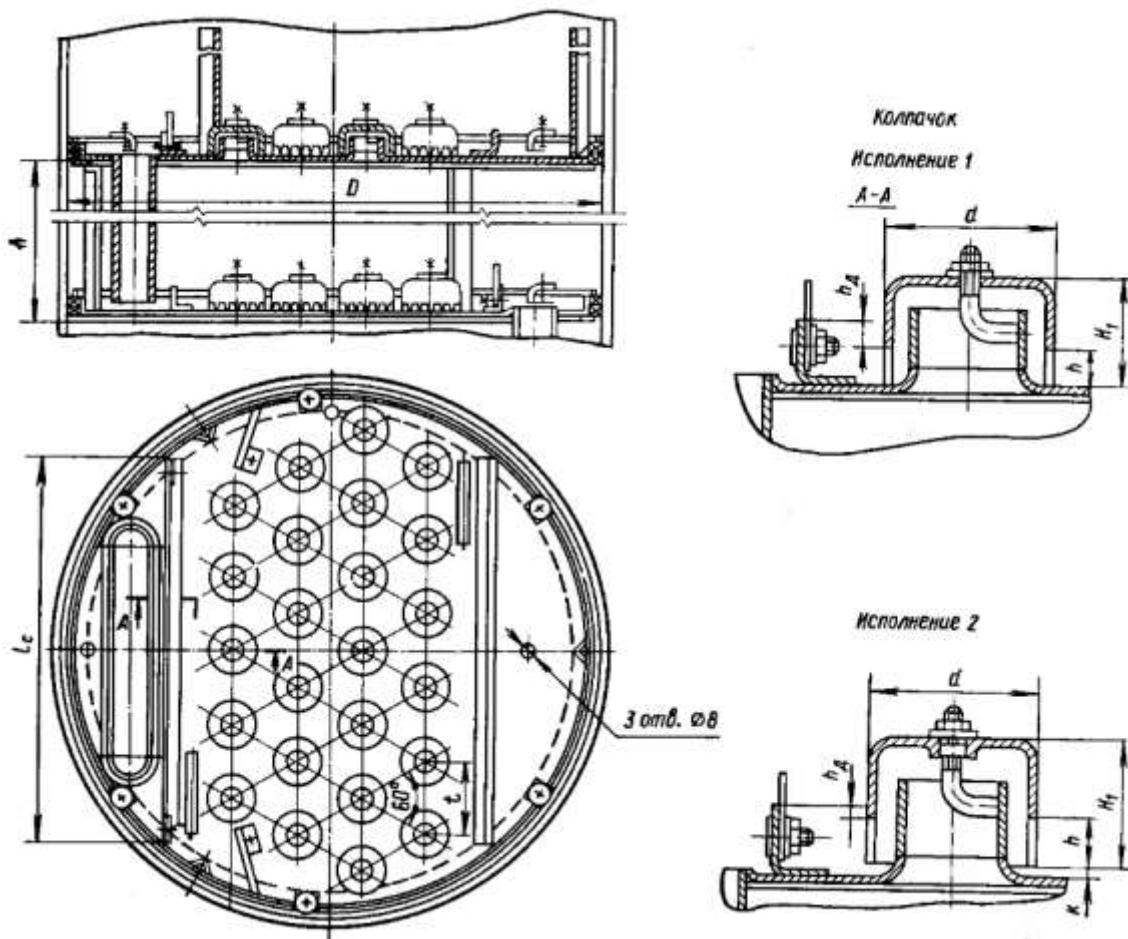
Ковпачкова тарілка типу ТСК-І
